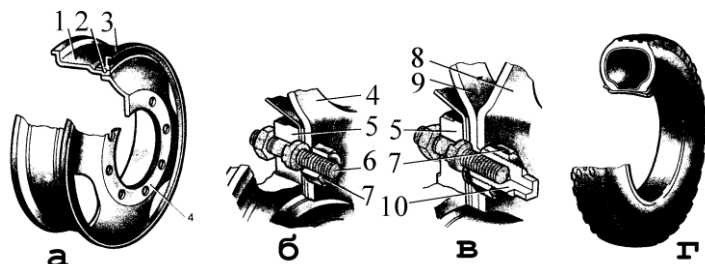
Колеса: а – дисковые; б – крепление диска переднего колеса; в – крепление диска заднего колеса; г – бездисковые; 1 – обод; 2 – разрезное съемное кольцо; 3 – неразрезное съемное кольцо; 4 – диск; 5 – ступица колеса; 6 – шпилька; 7 – гайка; 8 – диск наружного колеса; 9 – диск внутреннего колеса; 10 – колпачковая гайка
